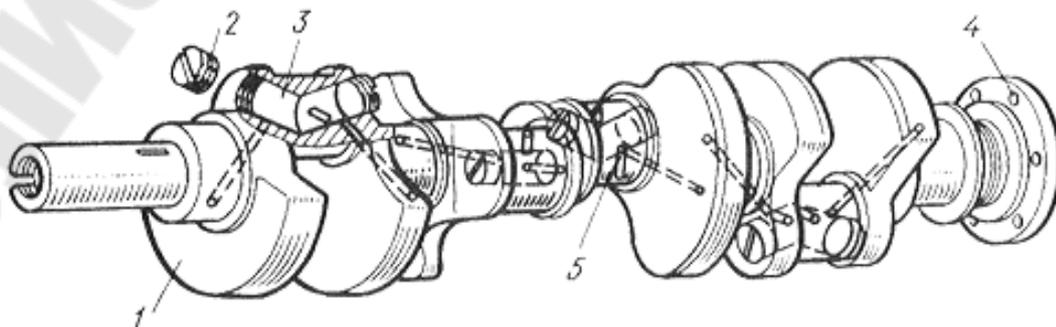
Коленчатый вал V – образного 8–цилиндрового двигателя ЗИЛ–130:
